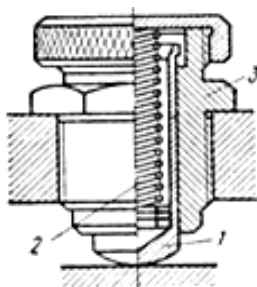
Пружинный прижим: 1 – упор; 2 – пружина; 3 – неподвижный стакан
